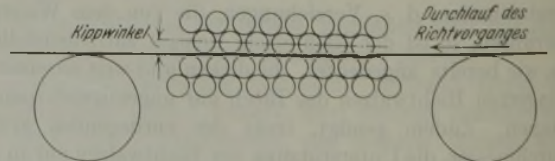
Warmblechrichtmaschine geschlossener Bauart mit kippbarer Oberwalzengruppe.
